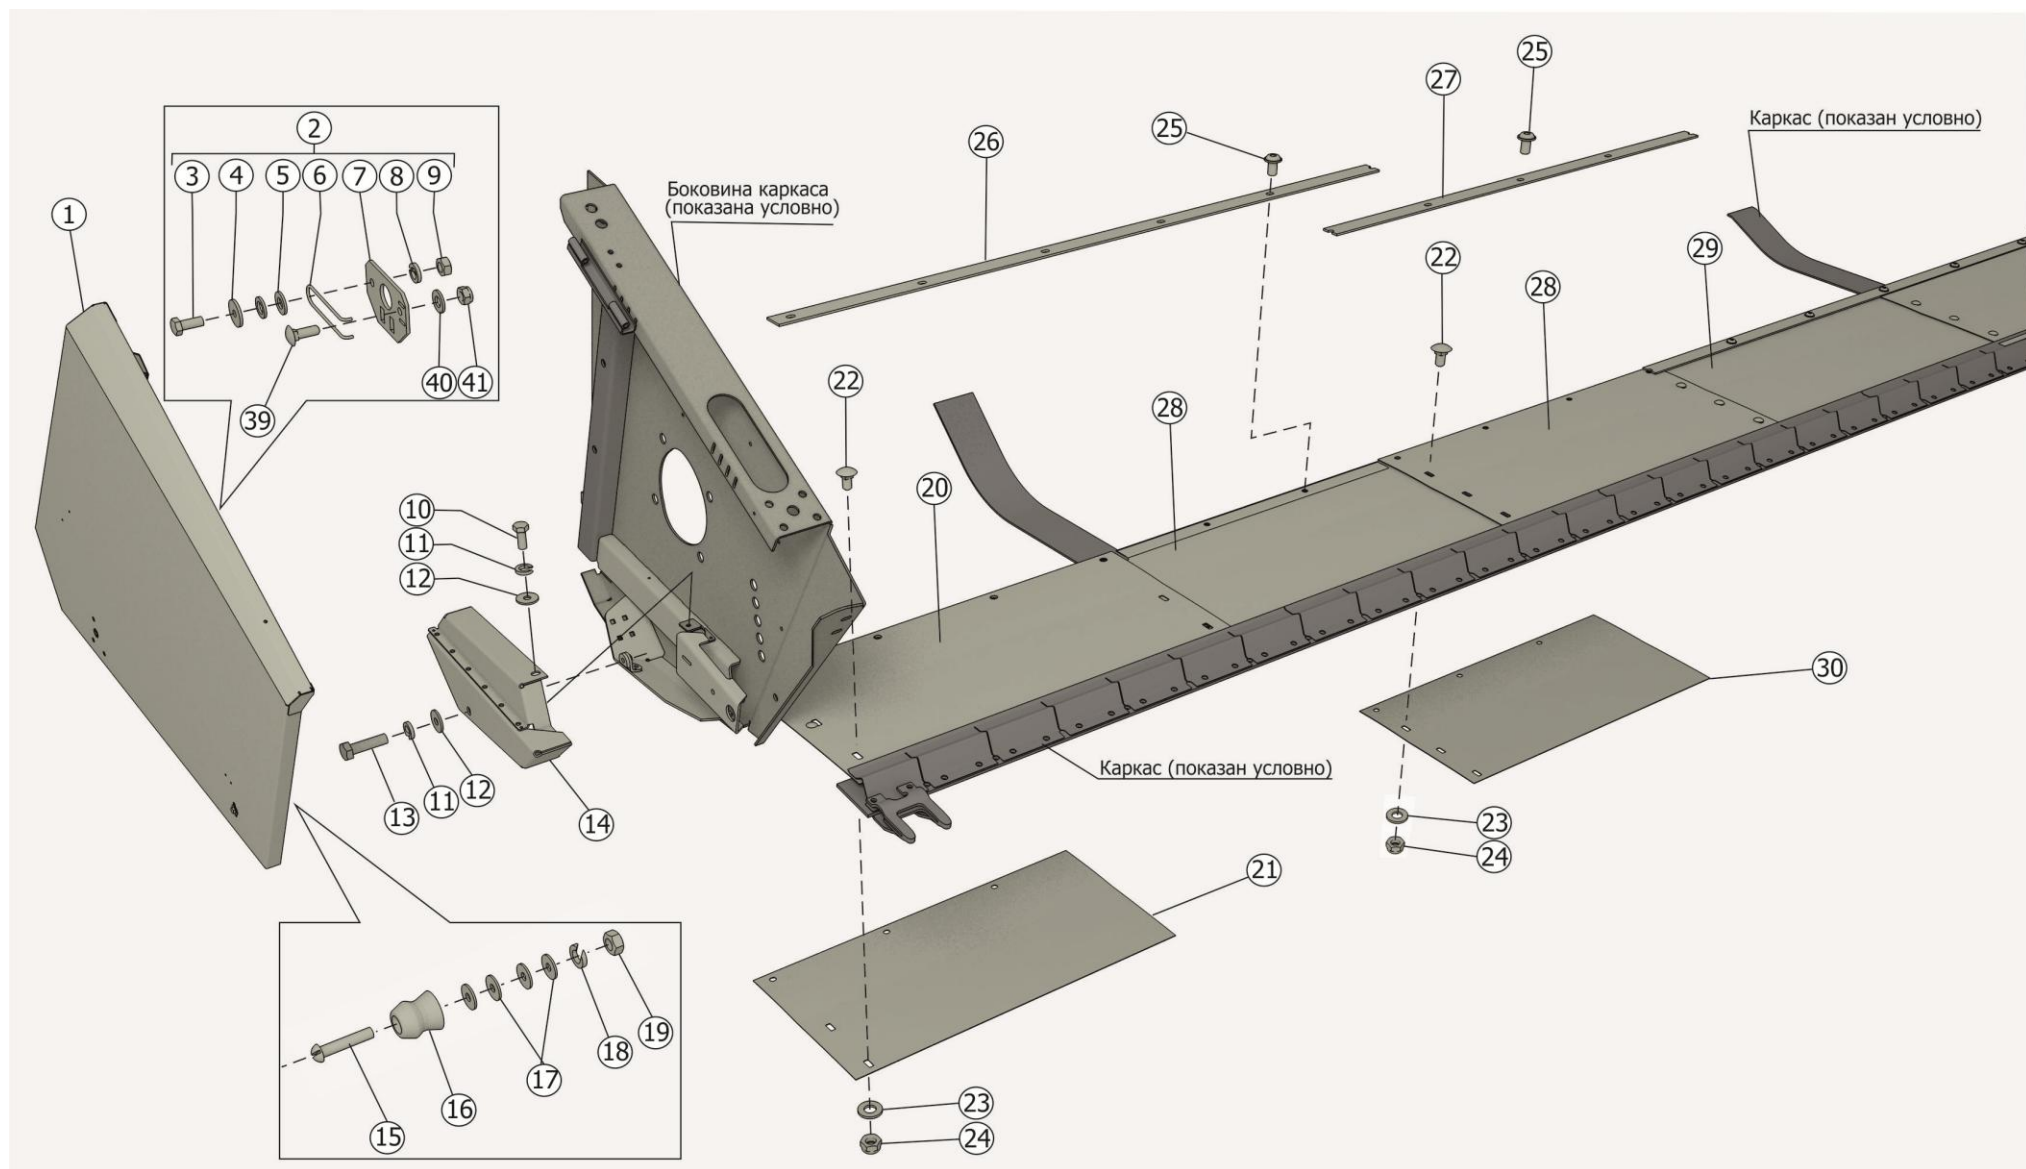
Установка щитков ЖСУ-703.11.00.000Б. Правая сторона
